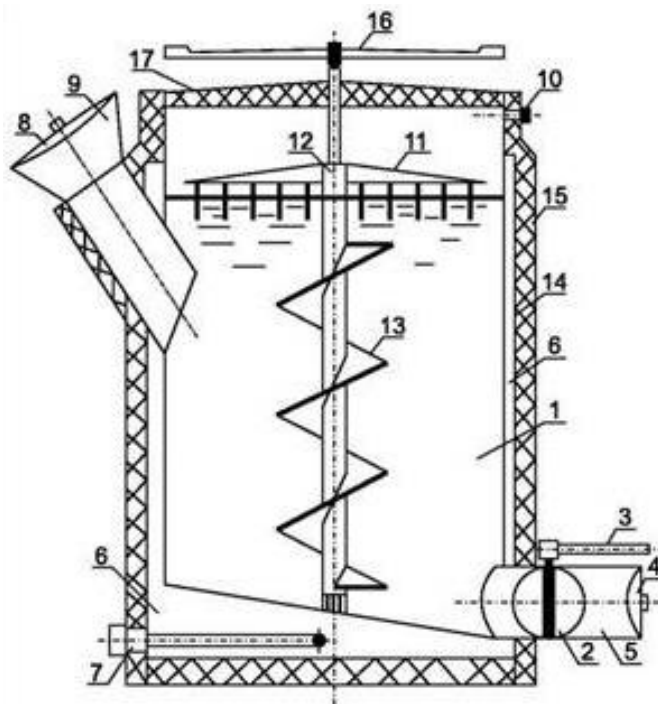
Схема биореактора-метантенка ИБГУ-1 в разрезе: 1 – корпус биореактора; 2 – диафрагма; 3 – рукоятка; 4, 8 – затвор; 5 – шлюз для выгрузки сброженной массы; 6 – корпус тепловой рубашки; 7 – ТЭН; 9 – загрузочный люк; 10 – газовый штуцер; 11 – гребенка; 12 – вал мешалки; 13 – шнек; 14 – облицовка теплоизоляции; 15 – теплоизоляция; 16 – рукоятка-крестовина мешалки; 17 – крышка биореактора.
